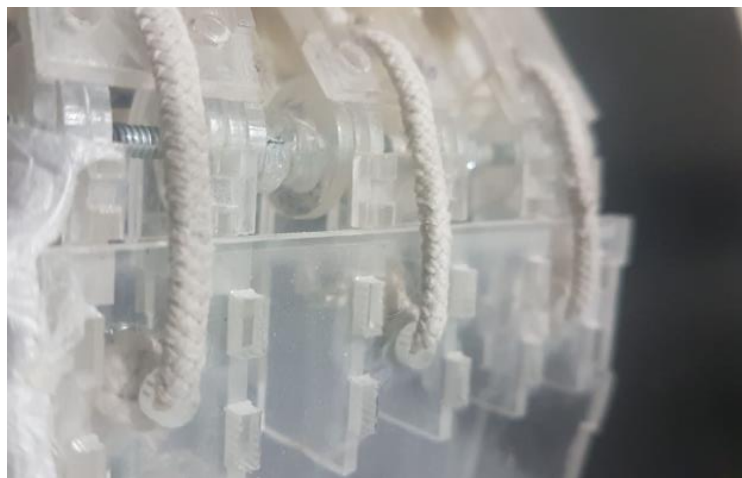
Soldando las piezas de la prótesis biomédica.
